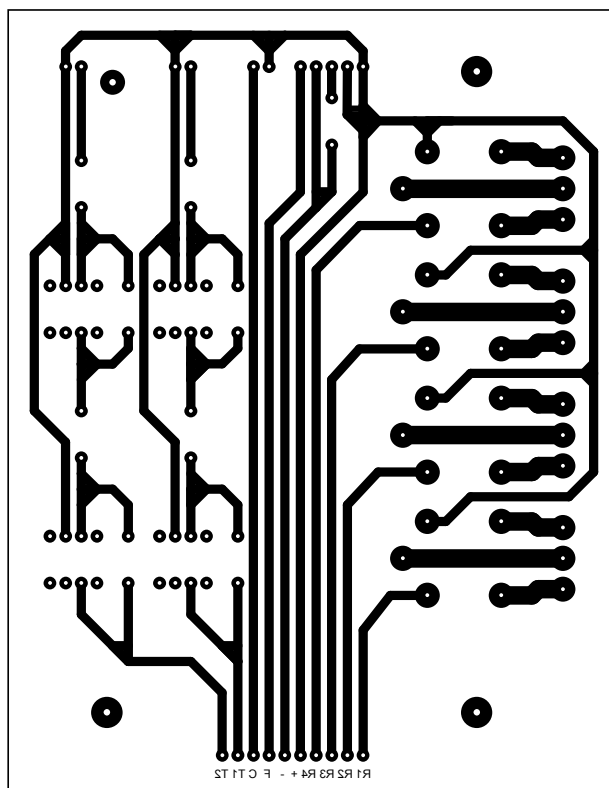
Imagen de capa de cobre del PCB para la primera versión del circuito con PCB.
